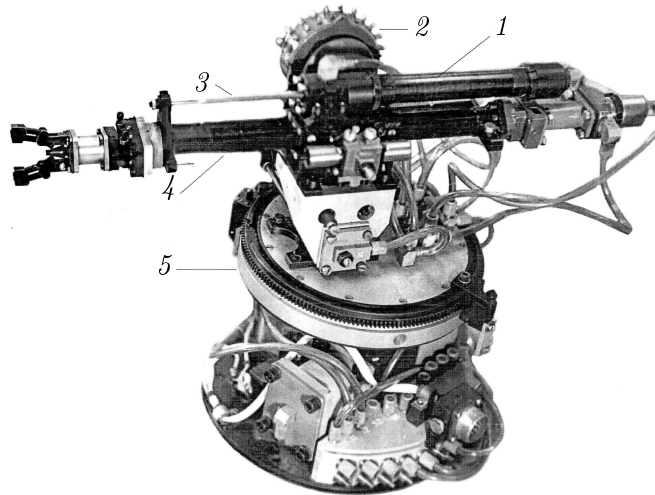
Макет следящего пневмопривода руки робота: 1 — пневмоцилиндр, 2 — датчик положения, 3 — шток, 4 — корпус механизма руки, 5 — поворотная платформа
